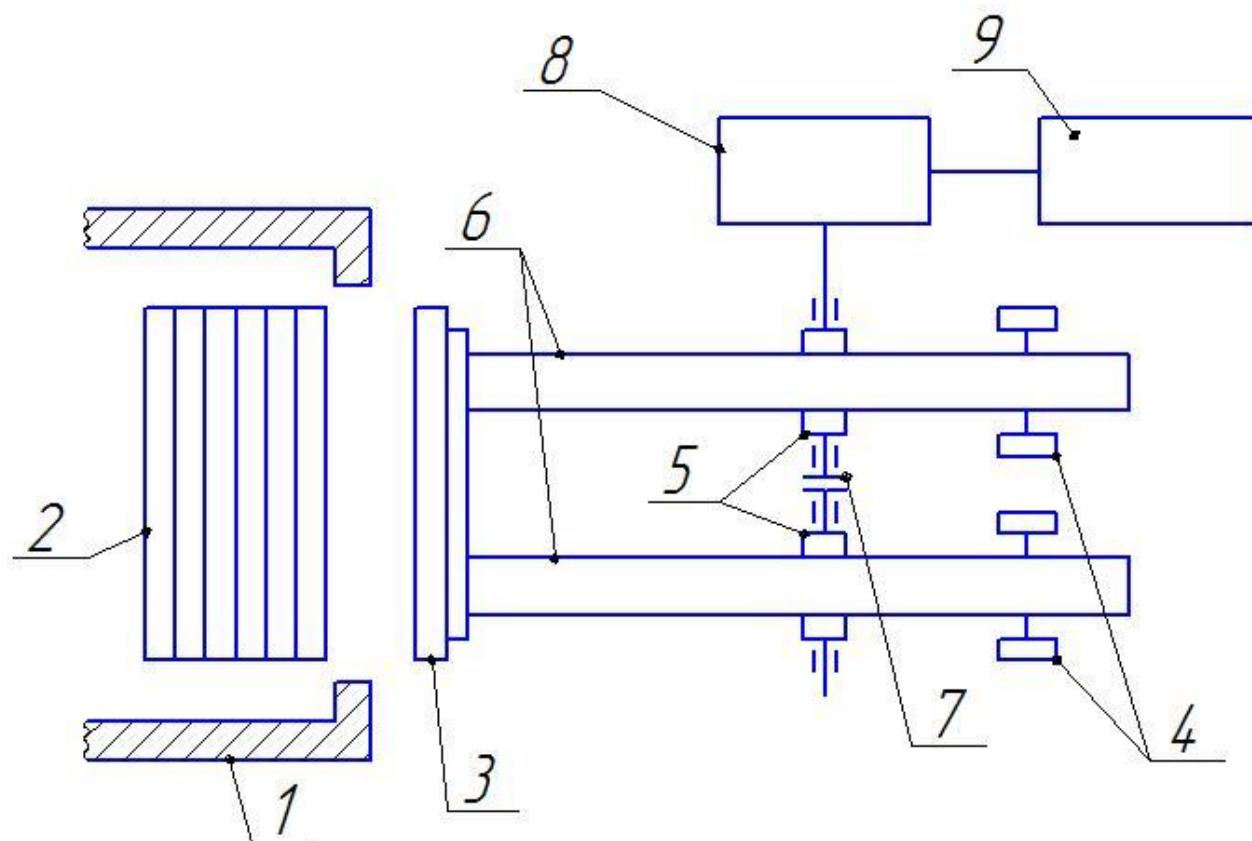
Принципиальная схема разрабатываемого толкателя
